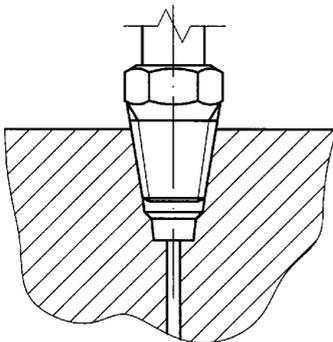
Kegelige Gewinde, Abdichtung im Gewinde
